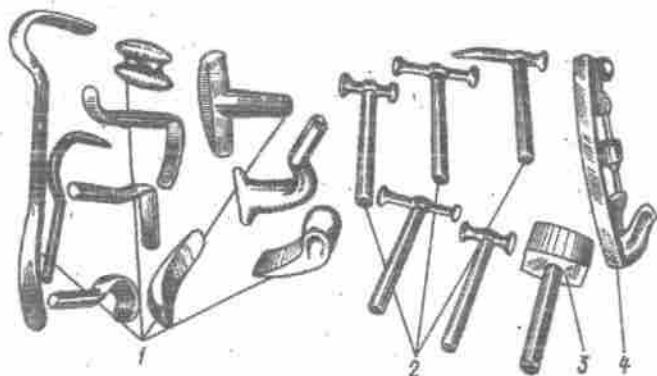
Werkzeugsatz zum Richten von Karosserie und Kabine:
